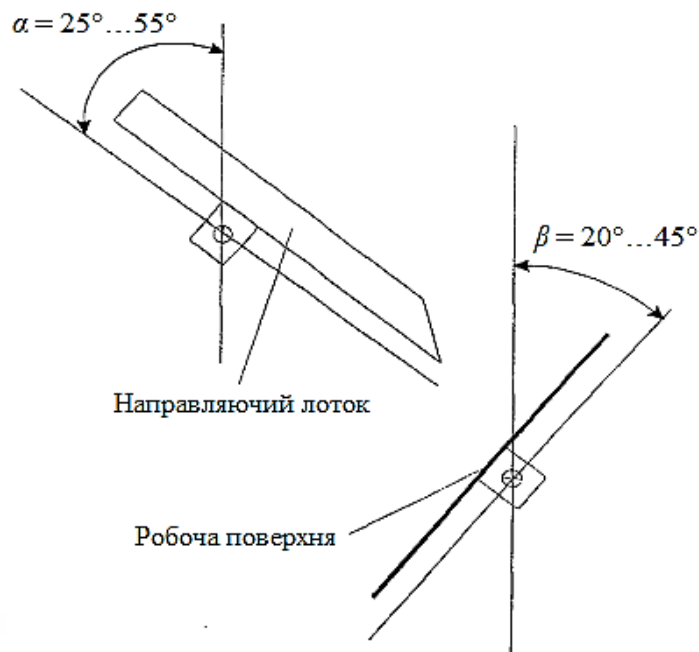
Кути установки лотка і робочої поверхні.
